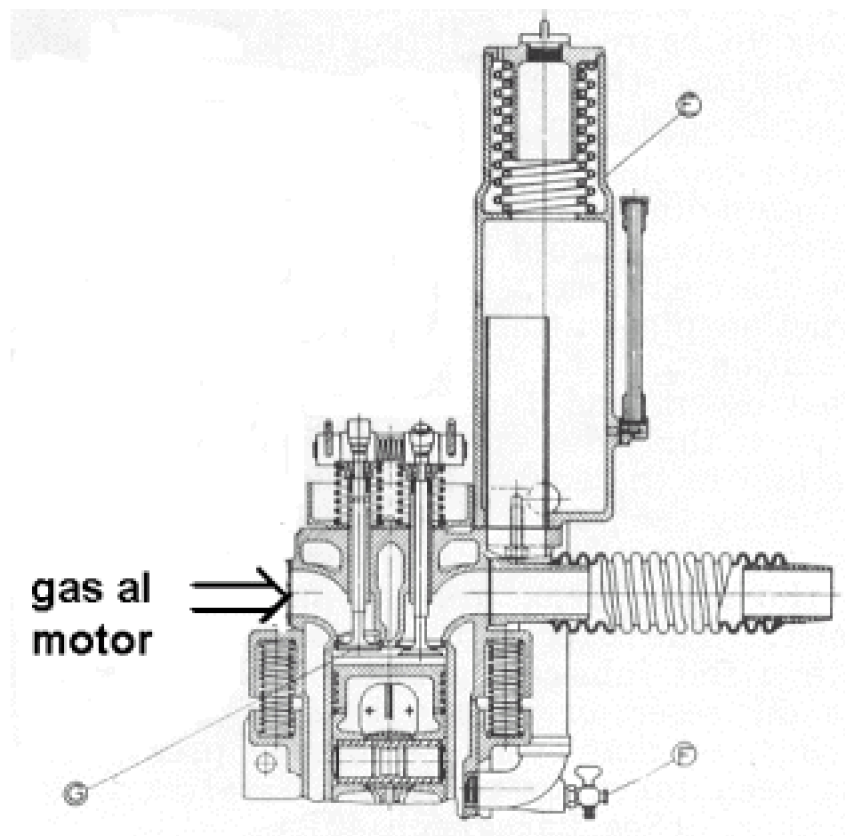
Sección parcial del motor que muestra entrada de gas al múltiple de admisión y cabeza del cilindro (ASTM - CFR, 1943)
